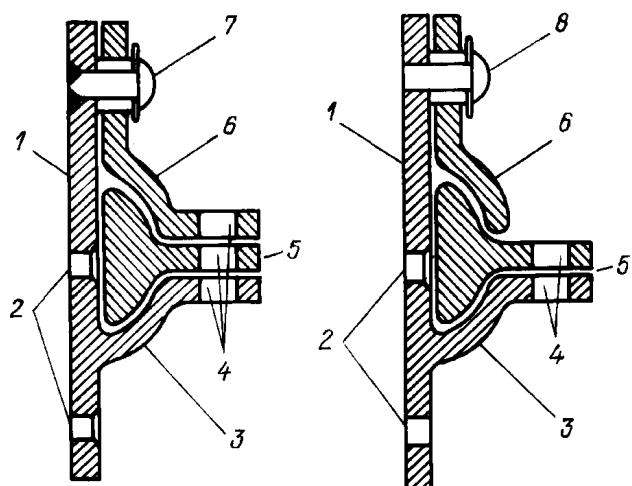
Приспособления для наложения таможенных печатей и пломб:
